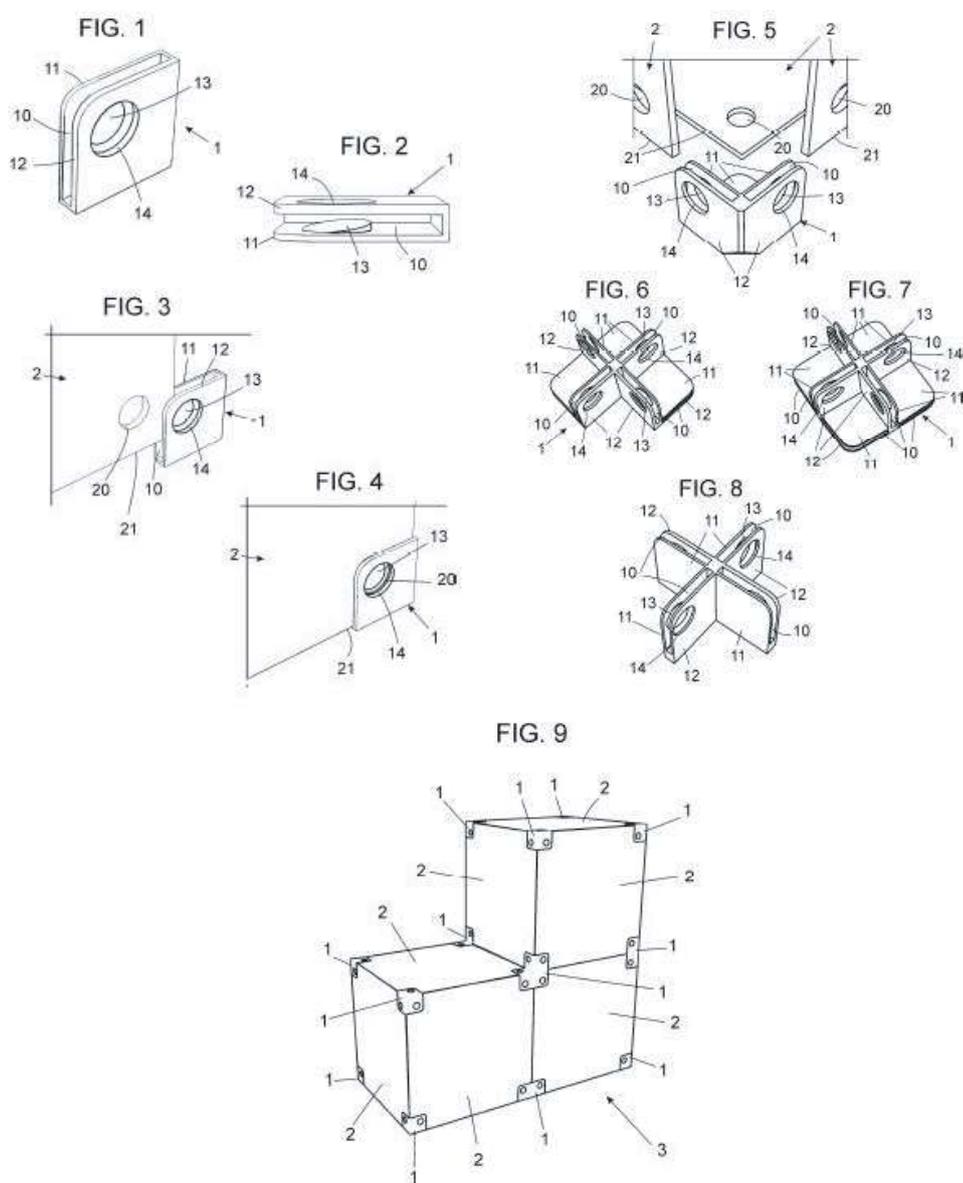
Estructura modular con ensamblaje por encaje a presión
